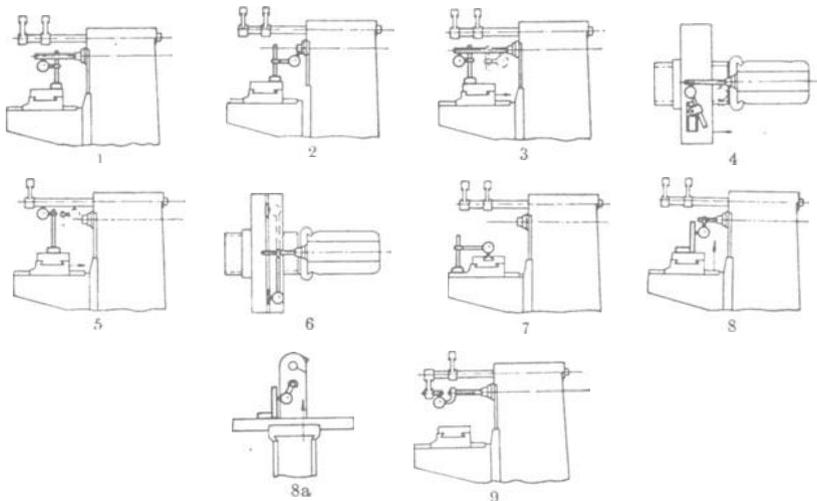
Prüftafel für eine Ständerfräsmaschine.
